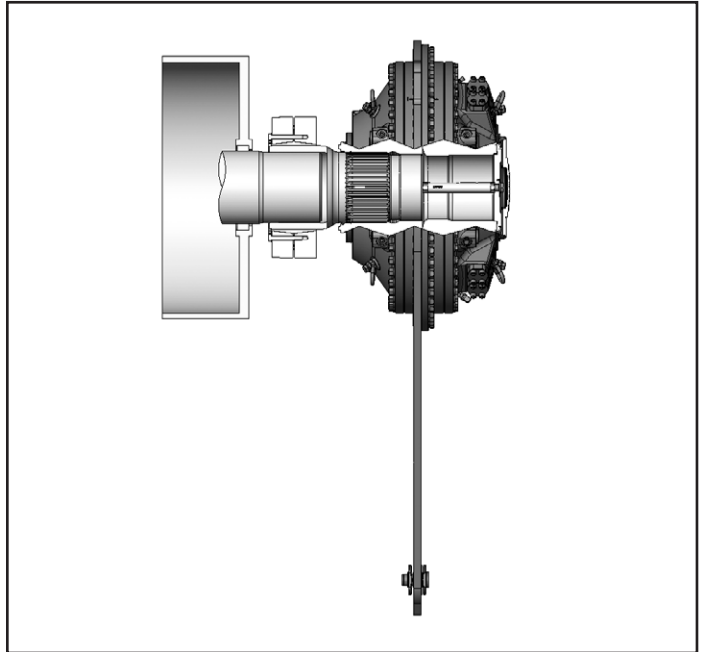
Motor mit Befestigung per Drehmomentstütze und Kupplungsadapter.
